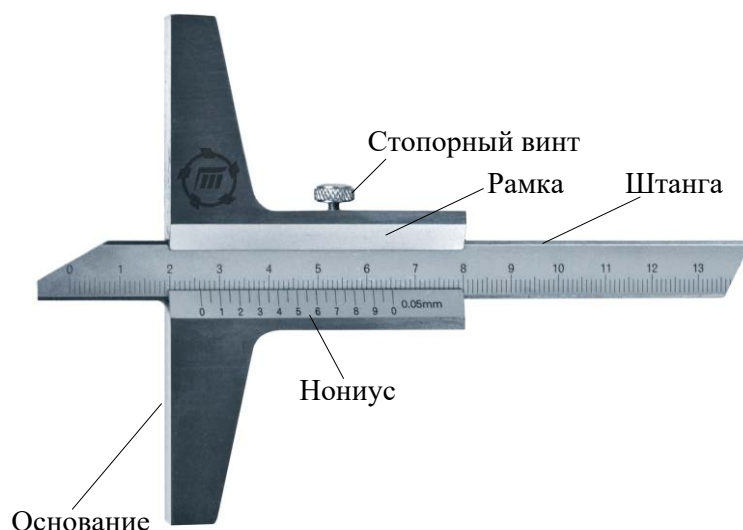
Внешний вид штангенглубиномера ШГ
